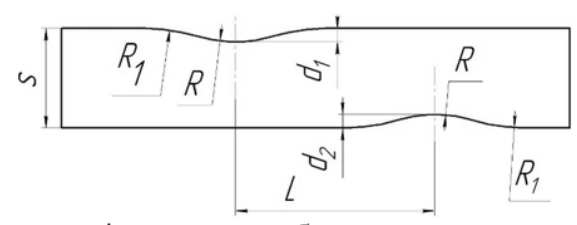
Геометричні параметри робочої зони зразка з неоднорідною товщиною
